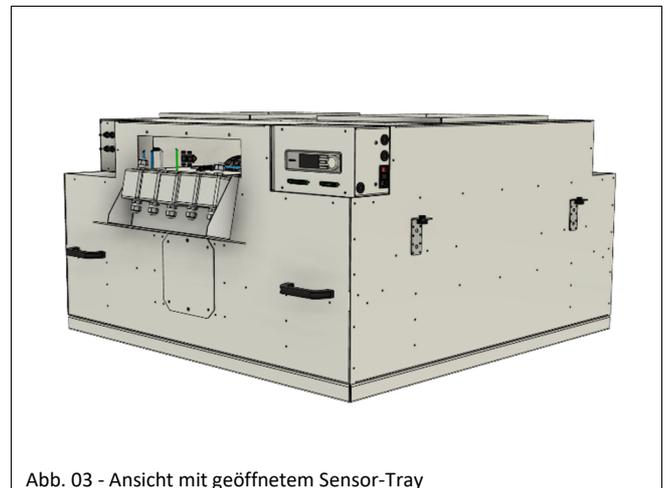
Ansicht mit geöffnetem Sensor-Tray
